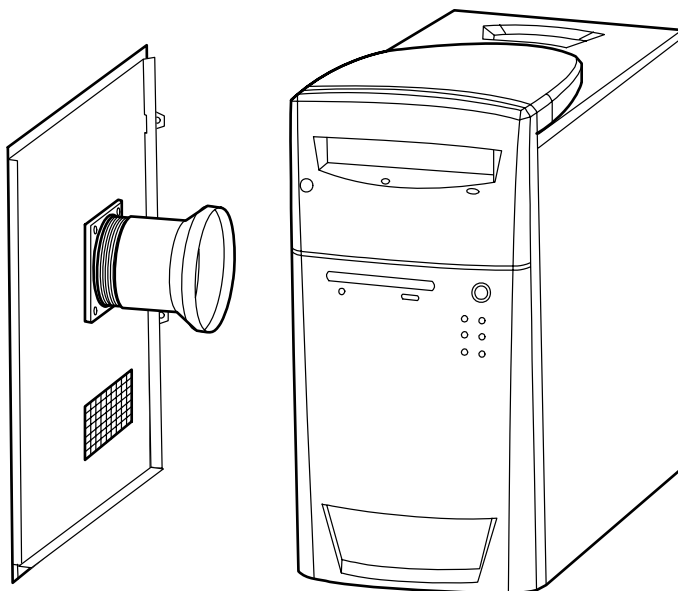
Стандарт корпусов с улучшенными температурными характеристиками предполагает наличие воздухозаборника и вентиляционного отверстия на боковой крышке
